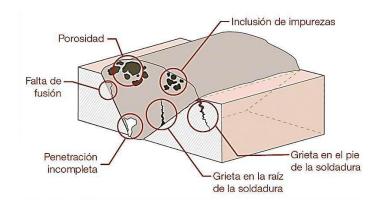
Discontinuidades de soldadura en juntas a tope
